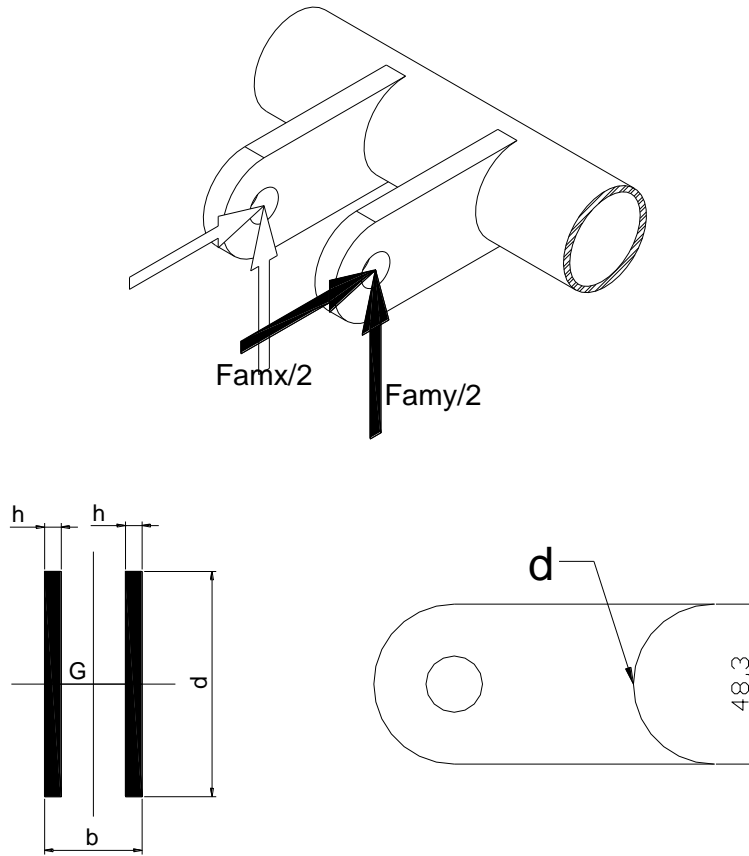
Soldadura anclaje superior amortiguador
